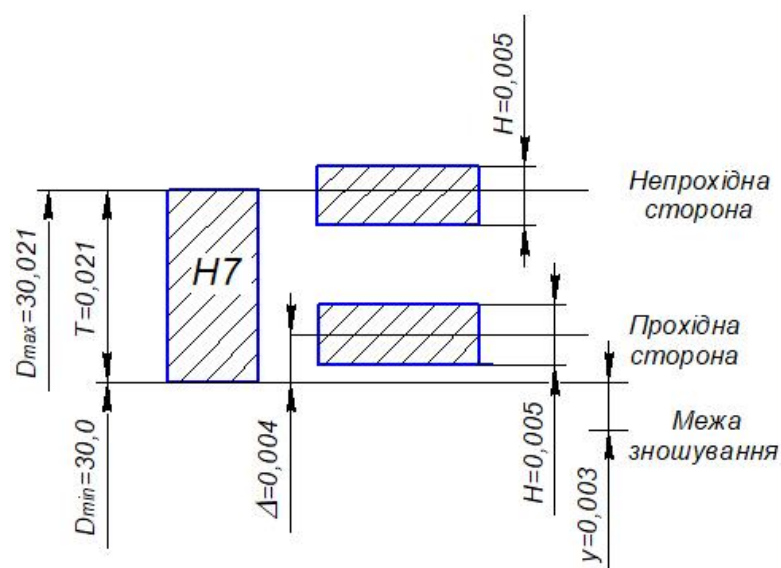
Поля допусків калібру-пробки
